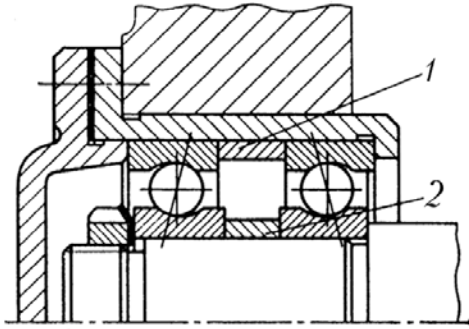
Схема узла с двумя спаренными подшипниками
